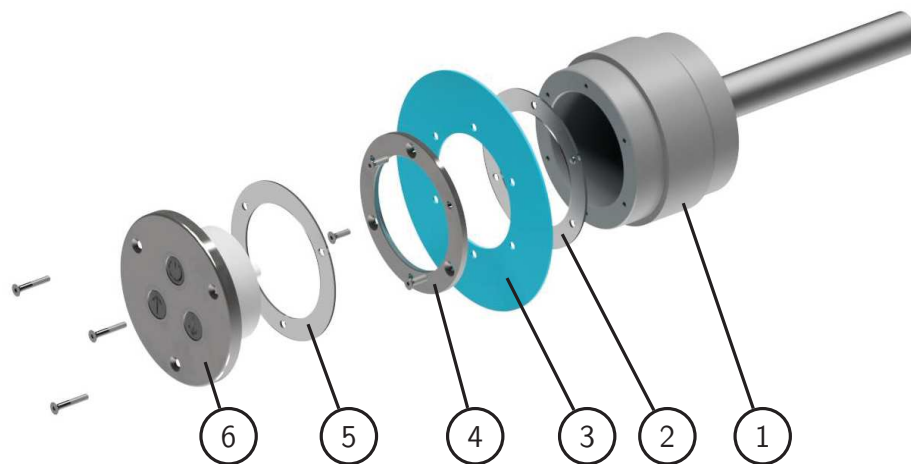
Explosionsansicht des Piezo-Schalters.
